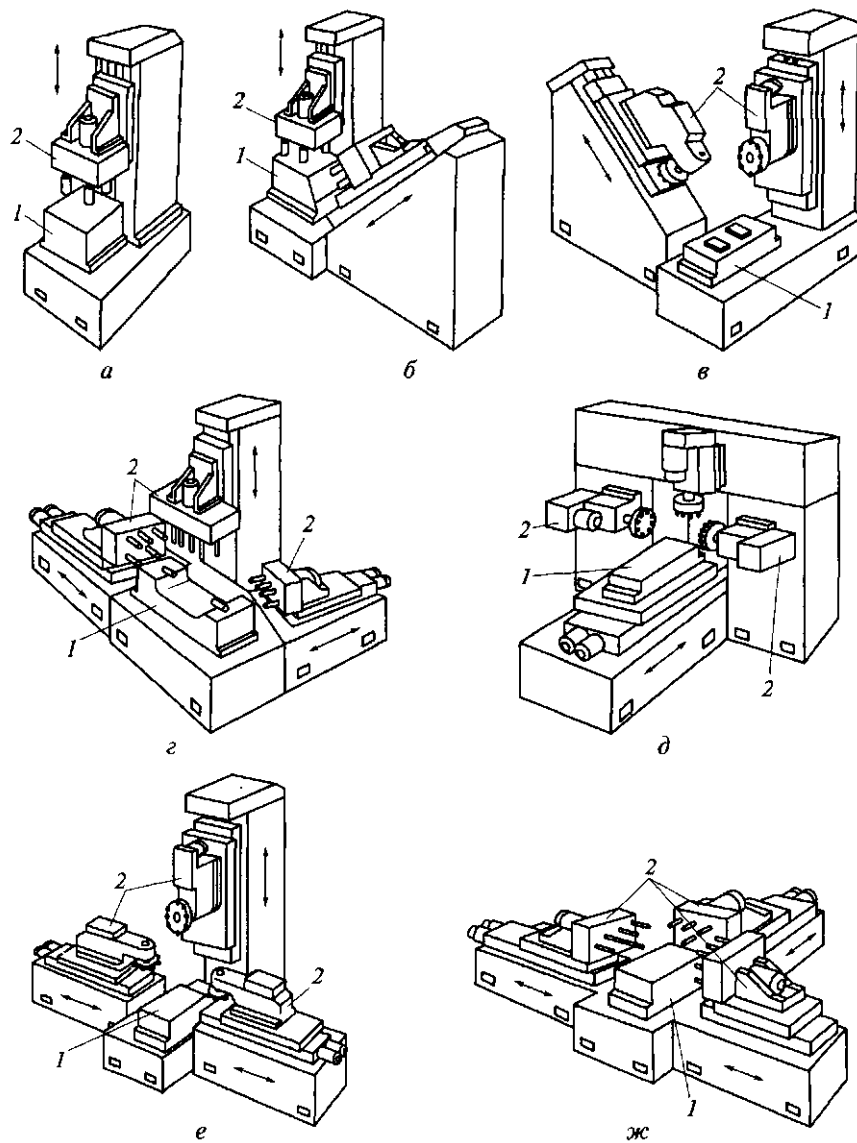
Типовые компоновки однопозиционных агрегатных станков со стационарным приспособлением для обработки заготовки с одной (а), двух (б, в) и трех (г—ж) сторон:
